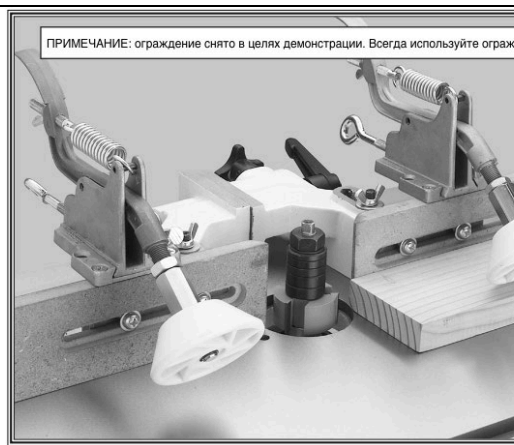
Используйте приспособление для того, чтобы прижимать заготовку.
